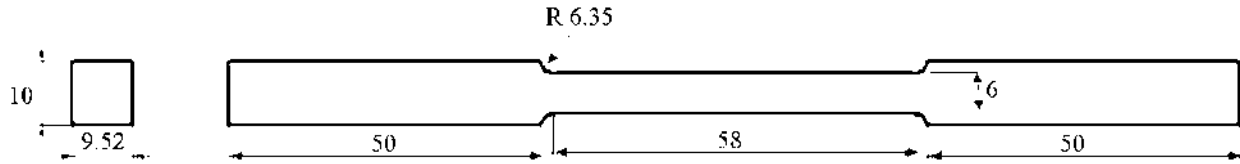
Dimensiones de probeta para ensayo de tensión (acotaciones en mm).
